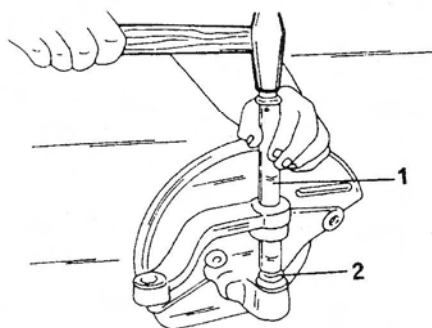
Установка втулки шкворня поворотного кулака. Для выдерживания глубины запрессовки стержнем (1) подложить распорную шайбу (2).
